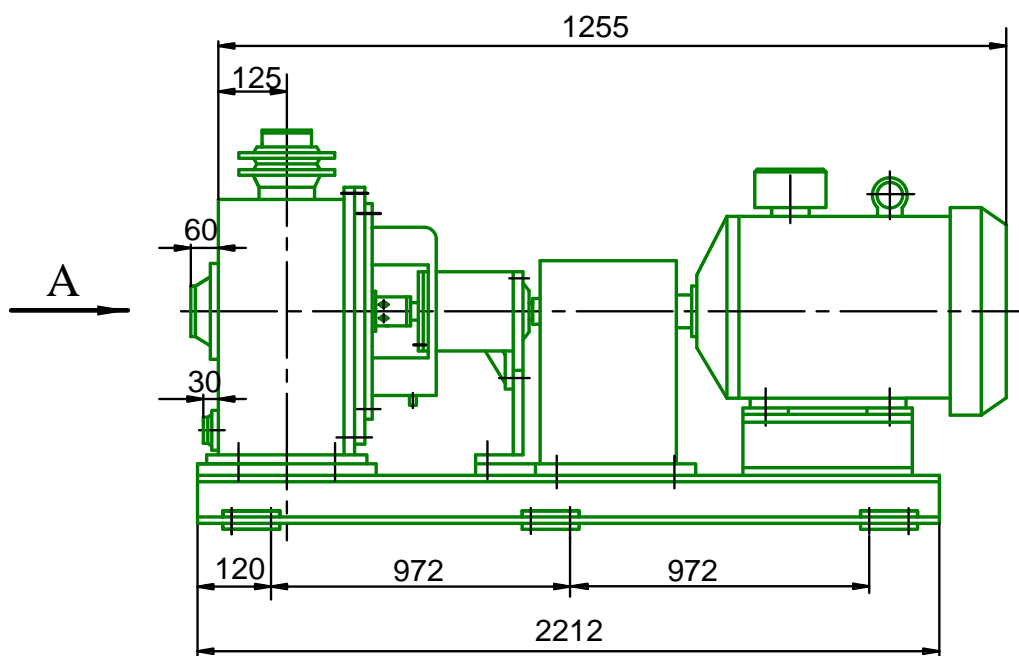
Габаритный чертеж насосного агрегата типа ЦНА 12,5/50
